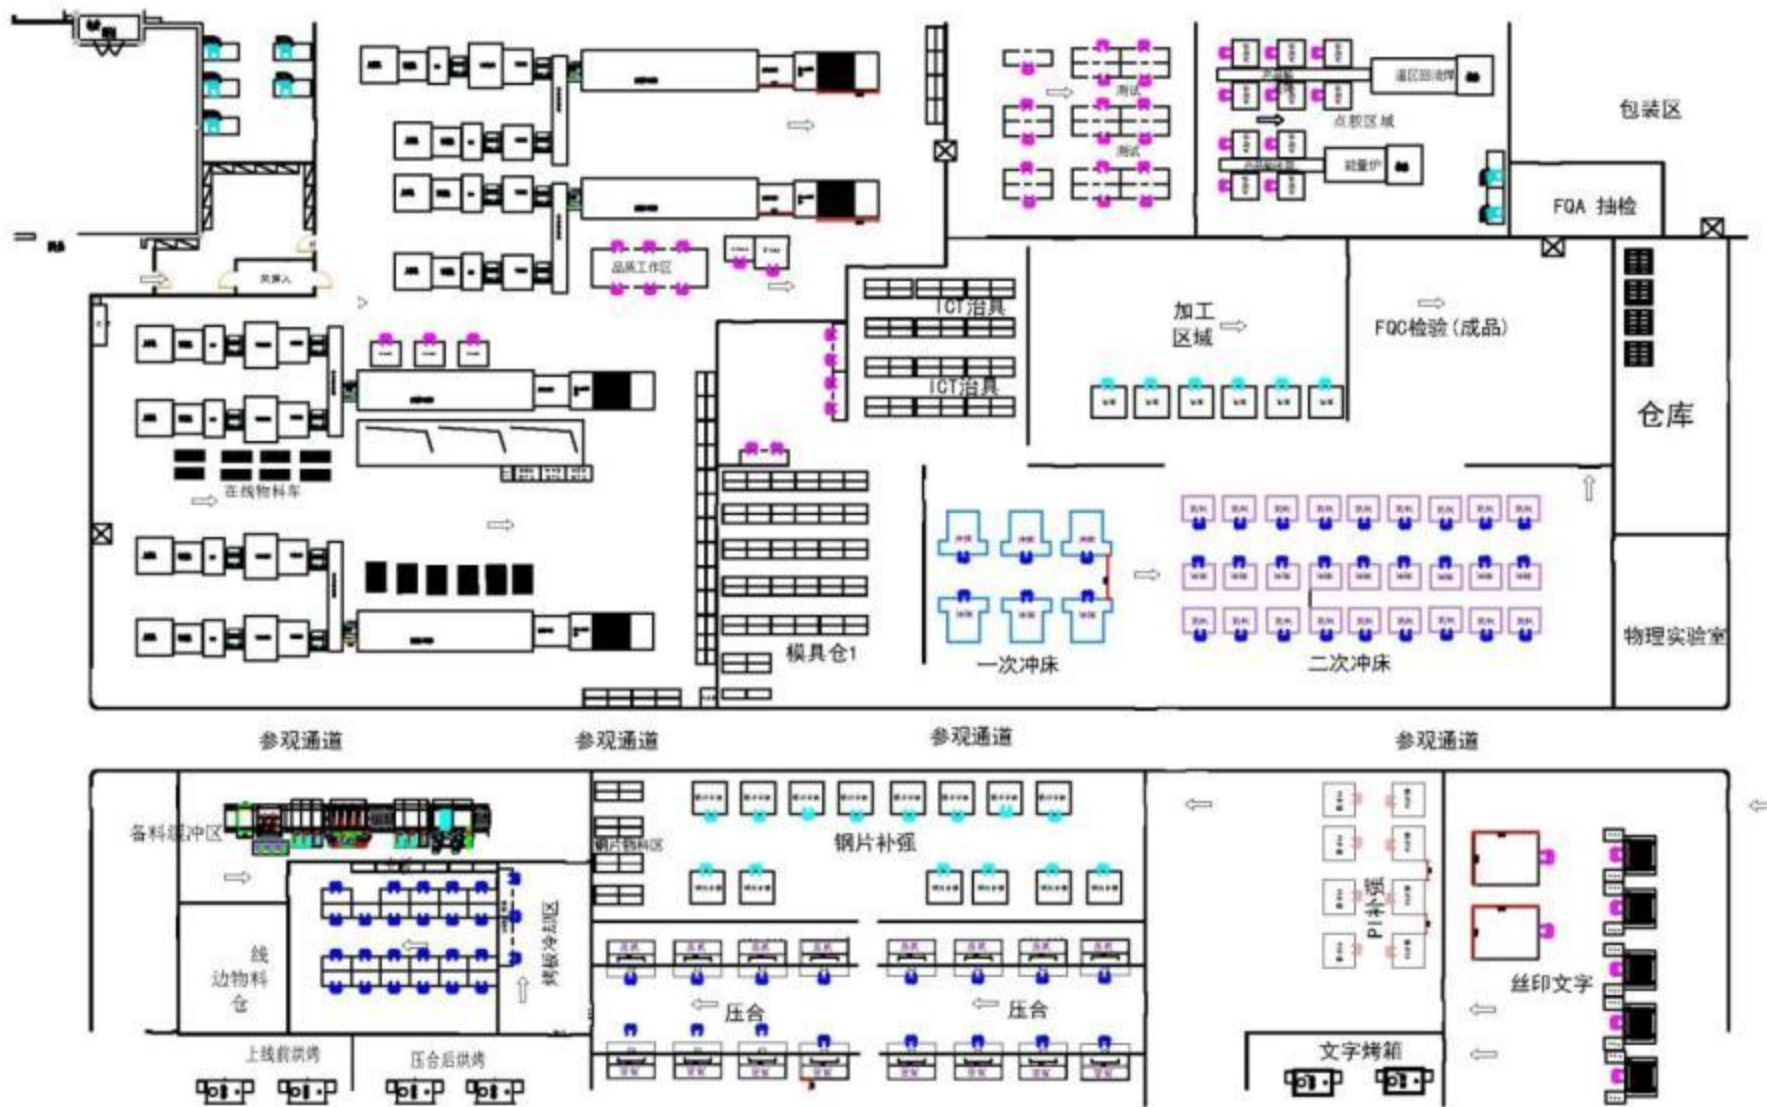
本项目二号厂房 7 楼环评阶段平面布置图
